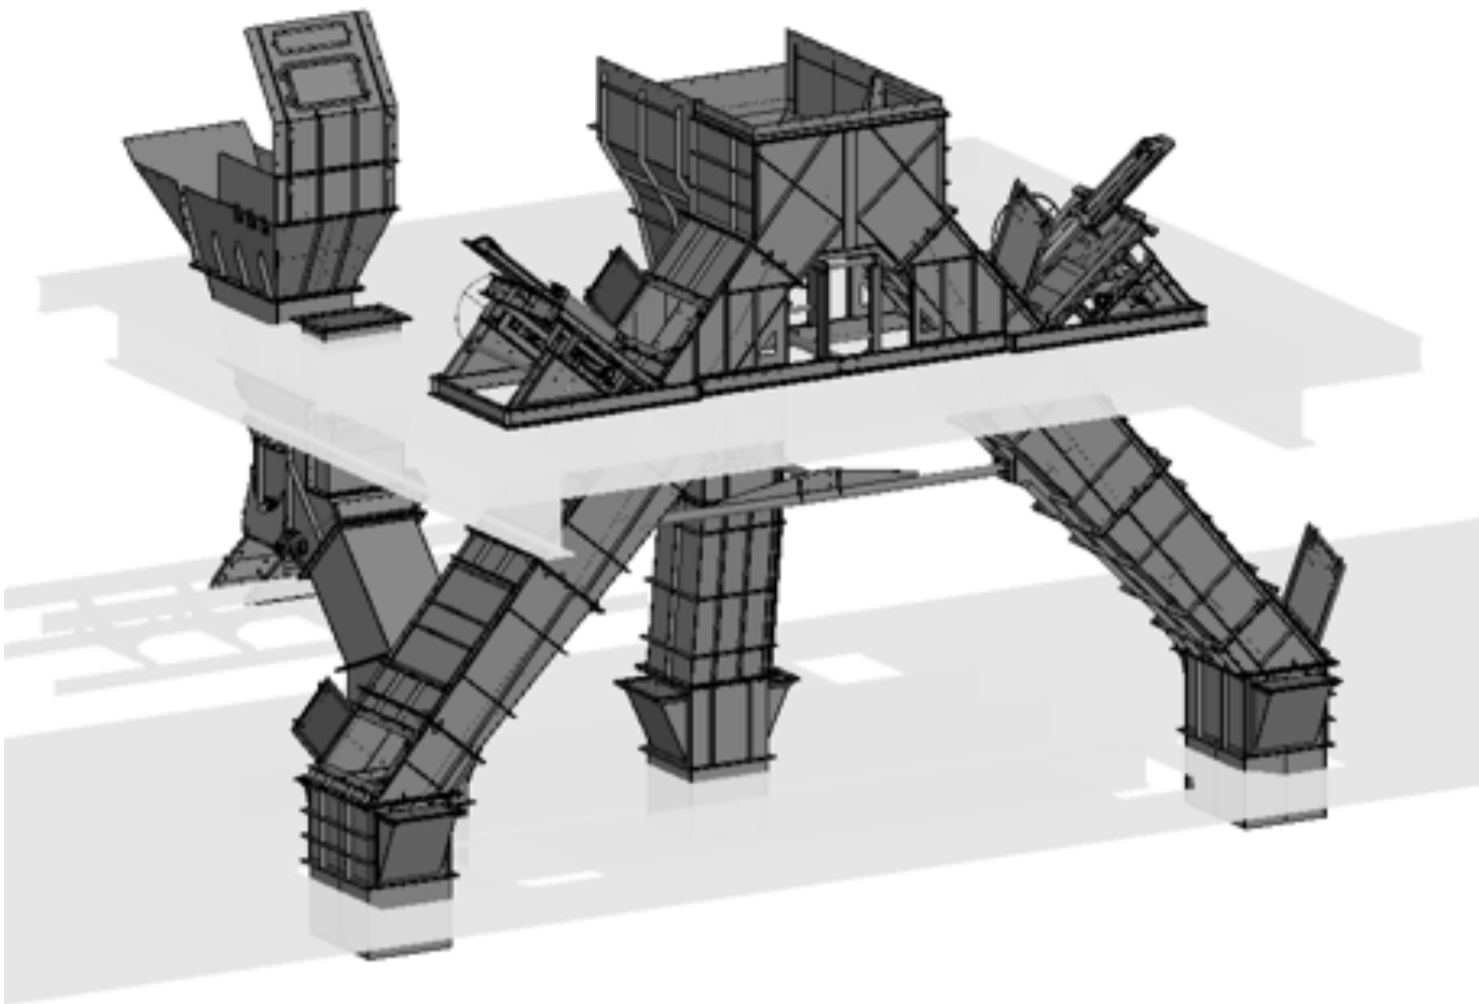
Zaprojektowana konstrukcja zabudowy podajników i przesiewaczy wibracyjnych - widok z prawej
